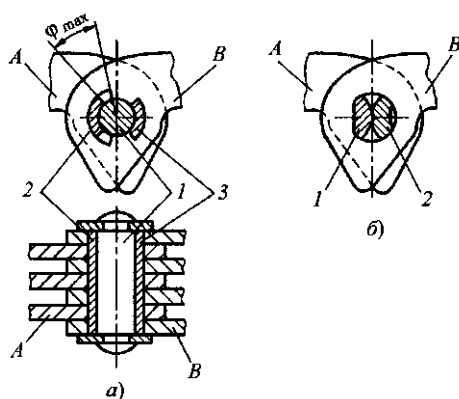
Шарнир качения зубчатой цепи
